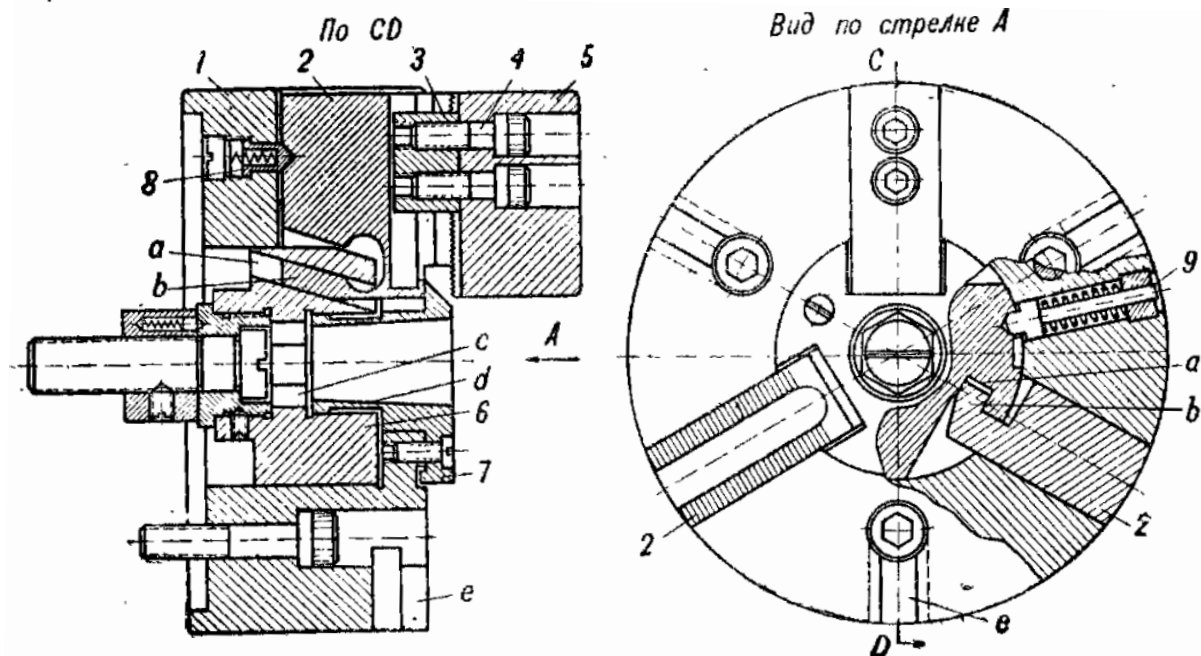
Трехкулачковый патрон типа Форкарт
